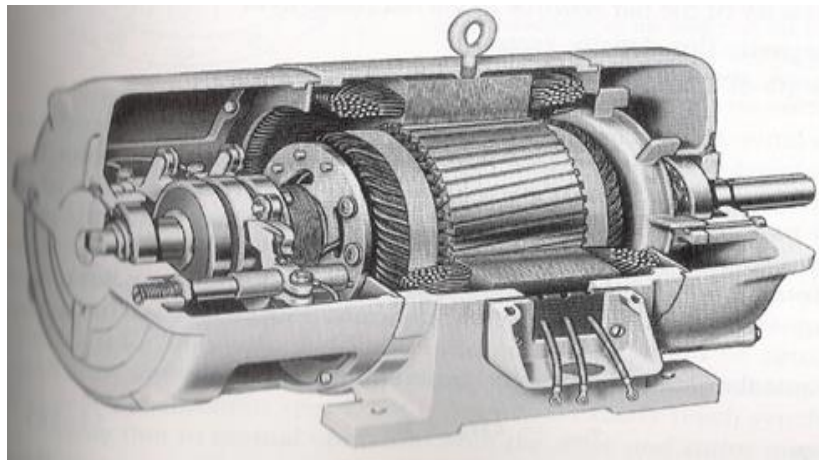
Coupe d'une machine asynchrone à rotor bobiné [44]
